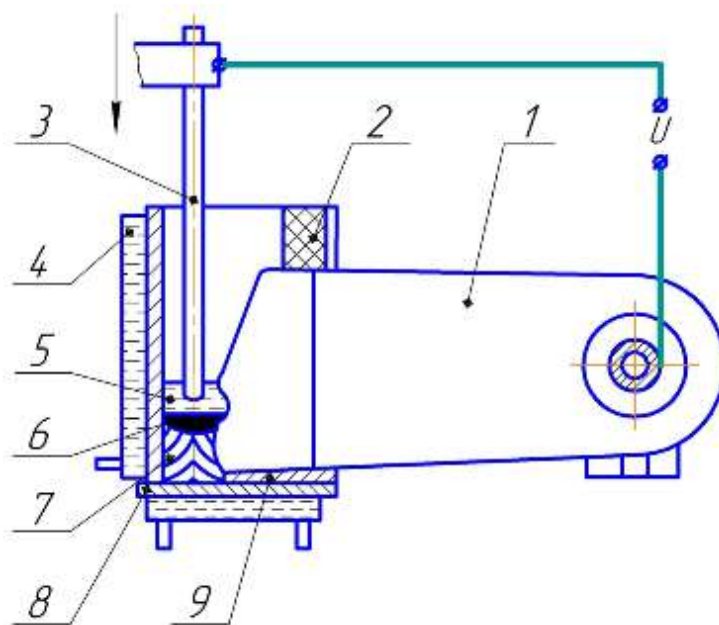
ЕШН молотка подрібнювача: 1 – наплавляюча заготівка; 2 – графітова вивідна планка; 3 - електрод; 4 – кристалізатор; 5 – шлакова ванна; 6 – металева ванна; 7 – наплавлений метал; 8 - піддон; 9 – вхідна мідна планка.
